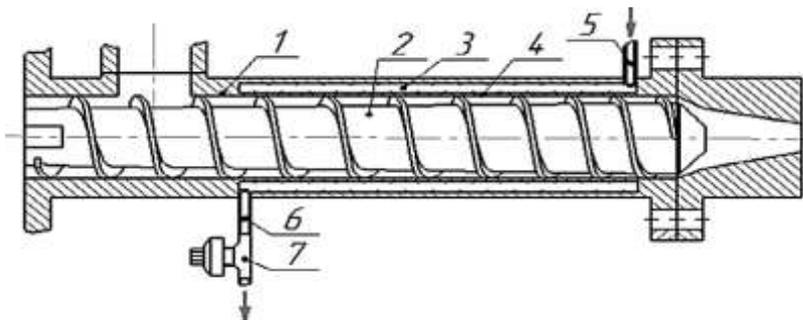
Узел термической переработки пластика (патент РФ № 193148): 1 - корпус экструзионной установки; 2 - шнек; 3 - нагреватель, выполненный в виде полого цилиндра; 4 - зона плавления; 5 - патрубок подвода пара; 6 - патрубок отвода конденсата; 7 - конденсатоотводчик
